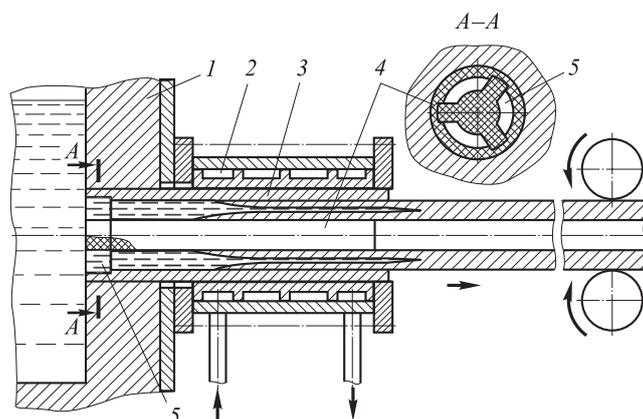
Кристаллизатор для горизонтального непрерывного литья трубчатых заготовок и профилей:
